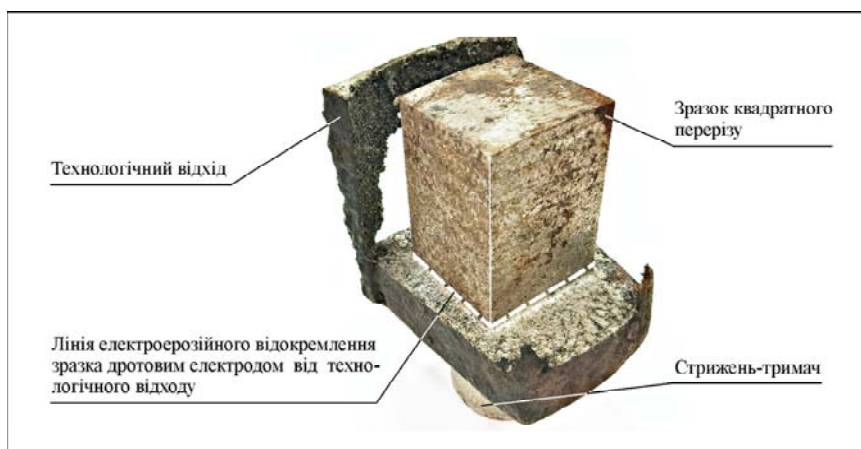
Зразок із ливарної сталі 110Г13Л після РОД
